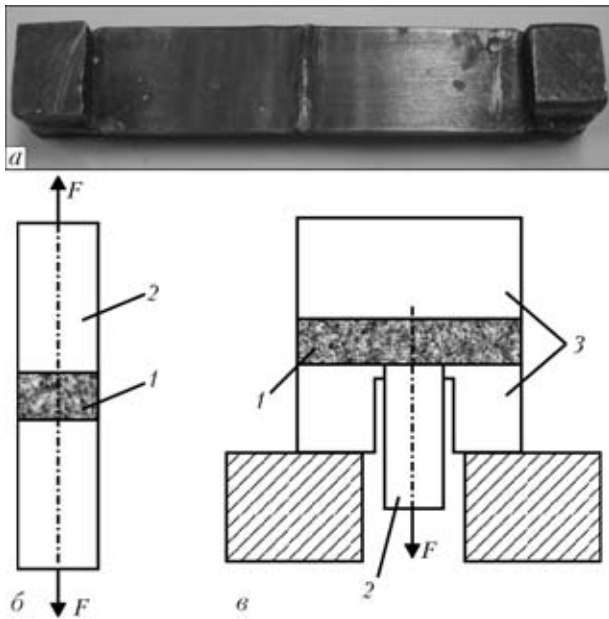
Образец основного типа (а) и схемы испытания на замедленное разрушение его (б) и специального образца (в) стыкового соединения: 1 — шов; 2 — рабочая (испытываемая) часть; 3 — вспомогательные части
